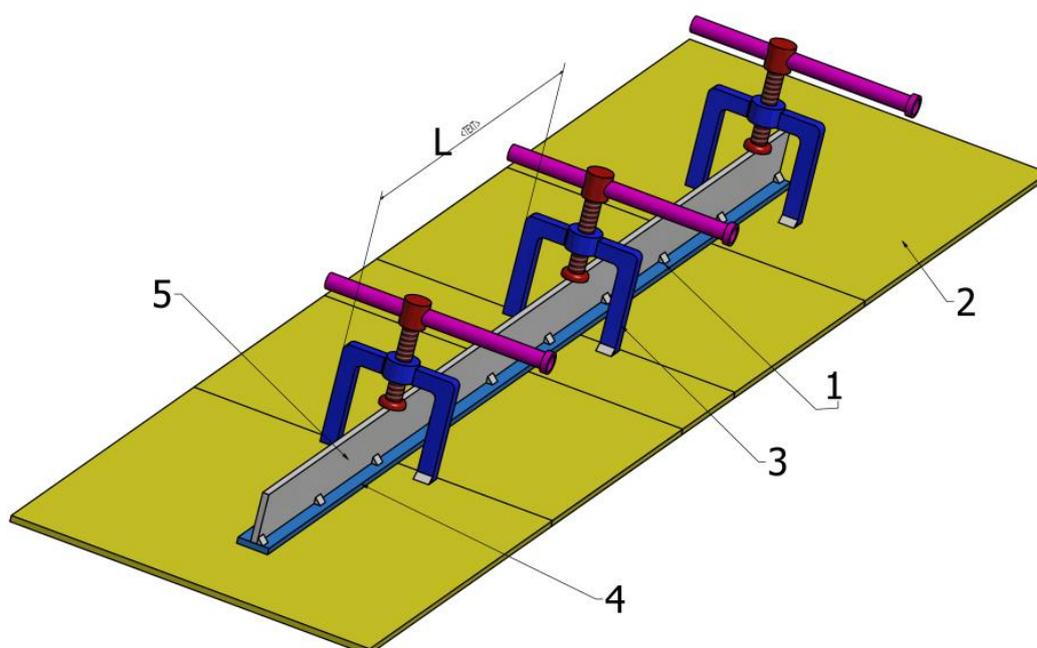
Сборка узла тавра с применением прижимов с П-образными приварными скобами. Рисунок автора.
